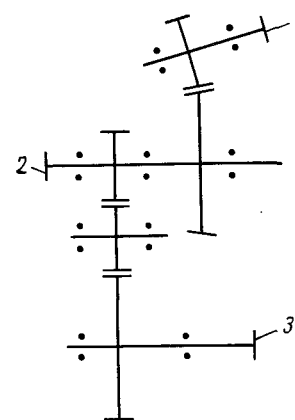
Схема редуктора ГТУ катера «Феросити»:
